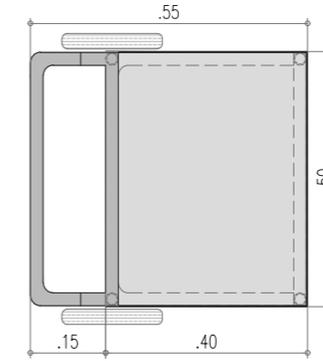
Planta puesto de venta ambulante tipo 3. Esc 1:15
